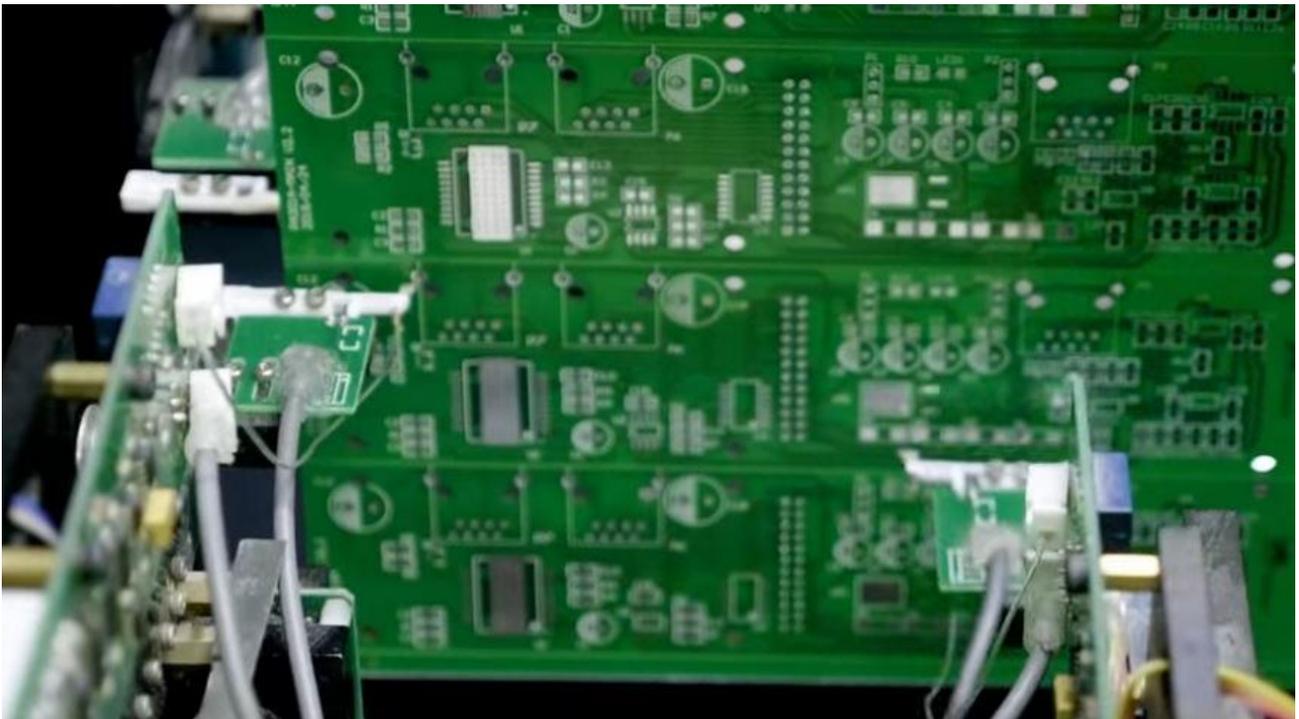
I due bracci della macchina automatica per il test di continuità elettrica.
